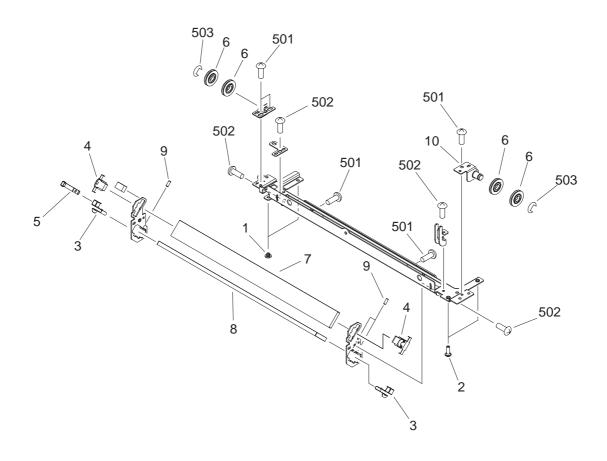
MIRROR ASSEMBLY 1 第1ミラー台部
